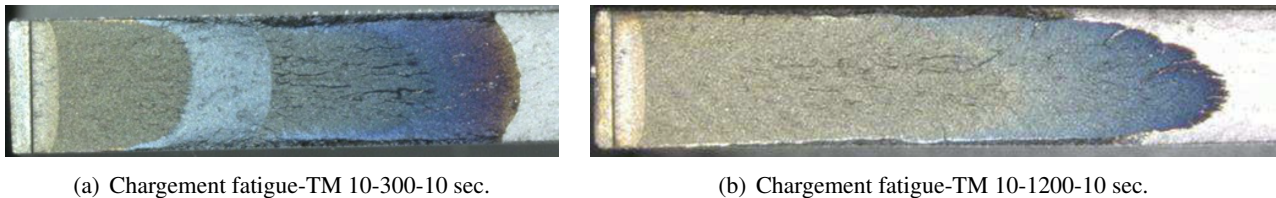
Courbure du front de fissuration à 550°C sur Inconel718 DA - éprouvettes SEN 2 mm [1].
